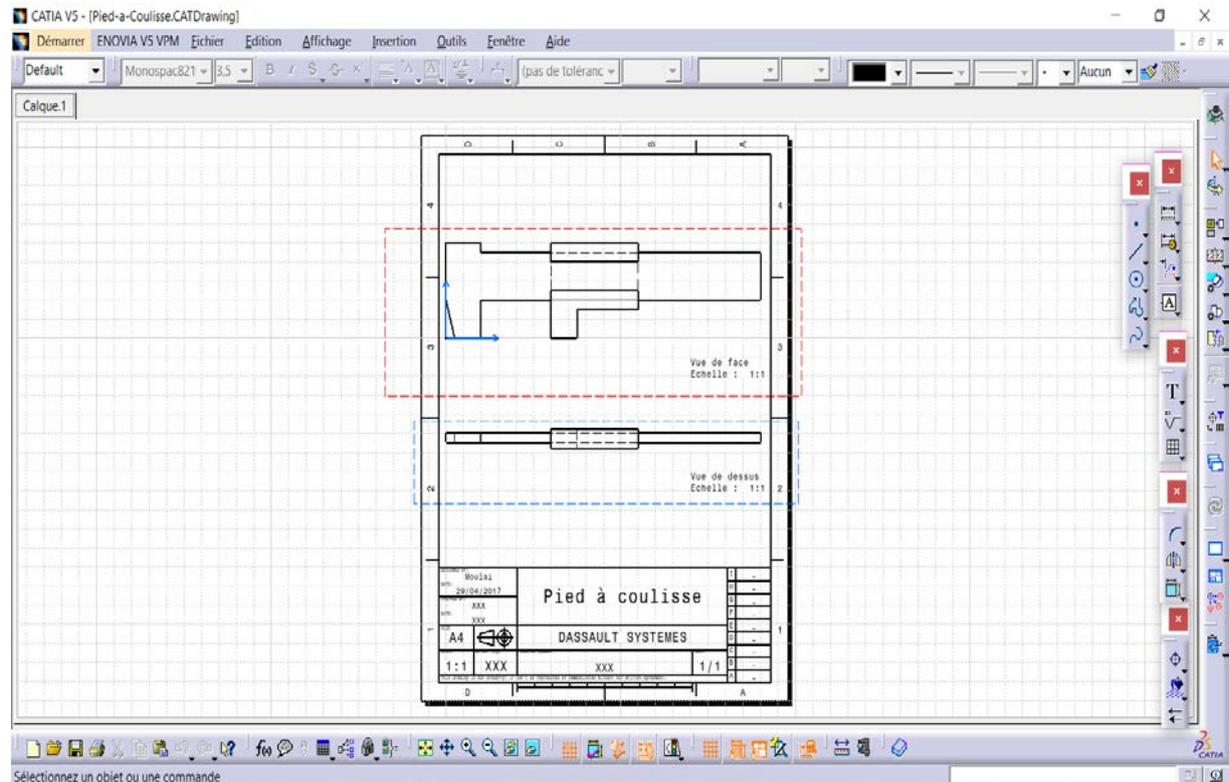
Drafting (mise en plan 2D) de l'assemblage Pied à coulisse [1], [2]
